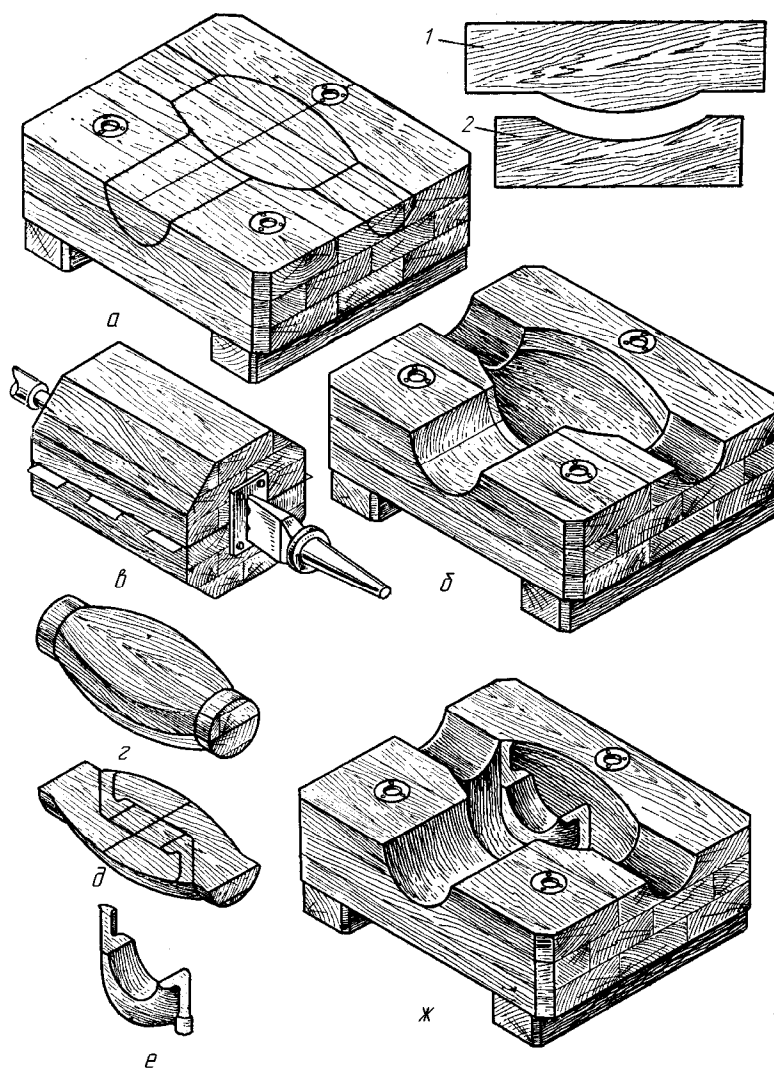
Процесс изготовления стержневого ящика для модели «Корпуса вентиля»
